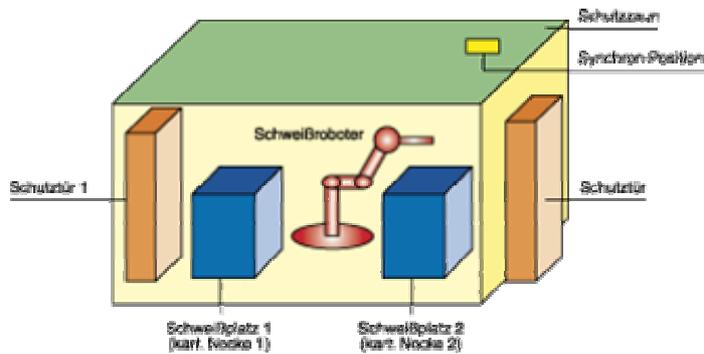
Dans l'exemple de cette cellule de soudage standard, les mouvements du robot sur les places de soudage 1 et 2 sont surveillés via les cames cartésiennes 1 et 2. Les contacts des portes de protection sont reliés aux cames cartésiennes du robot. Il y a déconnexion dès que le robot quitte la zone délimitée par les cames.
